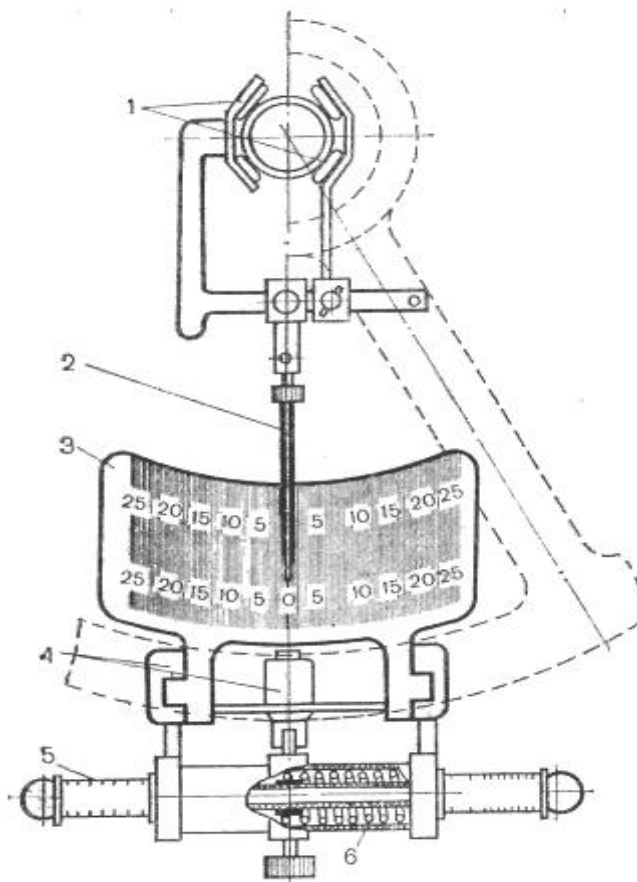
Прибор К-187: 1 – захваты рулевой колонки; 2 – указательная стрелка, закреплённая на валу рулевой колонки; 3 – шкала люфтомера; 4 – зажимы для крепления на рулевом колесе; 5 – динамометрическая рукоятка; 6 – пружина регулировки прибора.
